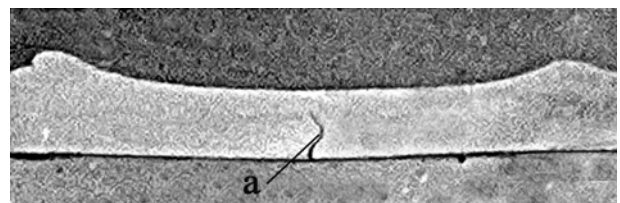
Макроструктура перетину зварного шву з дефектом, який подібний повздовжній тріщині (а)
